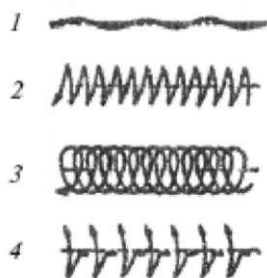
Способы перемещения мундштука горелки при газовой сварке: 1 - незначительными колебаниями при сварке малых толщин; 2—полумесяцем; 3 — петлеобразно; 4 - полумесяцем с задержкой вдоль шва
